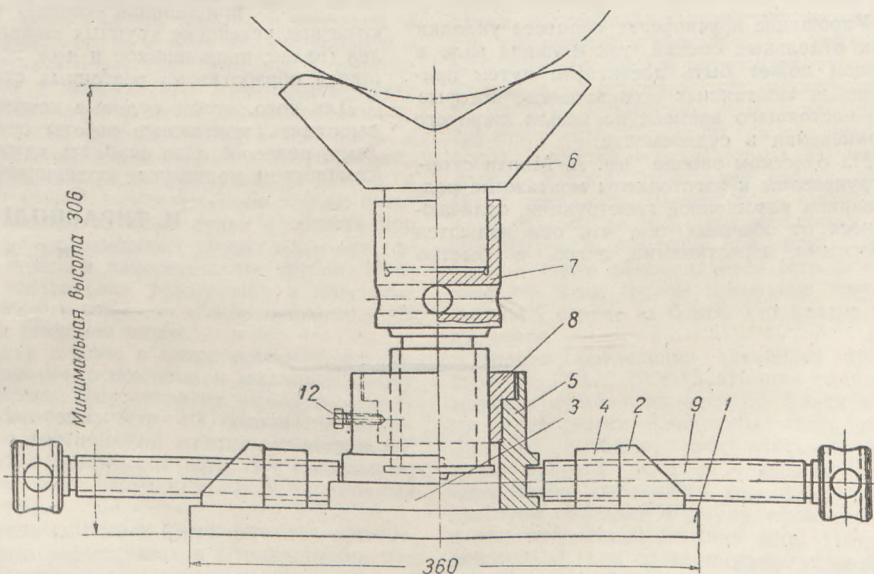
1 — плита; 2 — упорный угольник; 3 — направляющая планка; 4 — планка отжимного болта; 5 — стакан; 6 — седло; 7 — подъемный винт; 8 — гайка подъемного винта; 9 — шайба; 10 — отжимной болт; 11 — винт M12×16; 12 — винт M12×35 (стопор)
